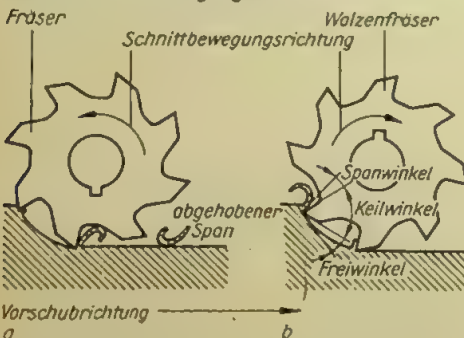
a Gleichlauf- und b Gegenlauf-Fräsen
